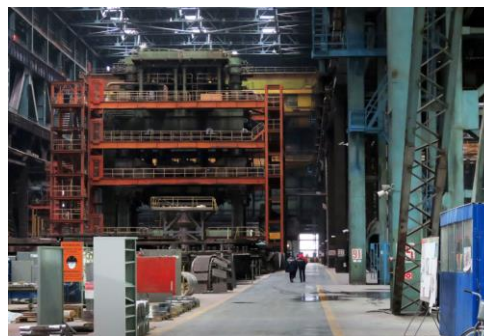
Пресс «ИИ» усилием 15000 тонн (Япония), предназначенный для изготовления изделий методом горячей штамповки¹
